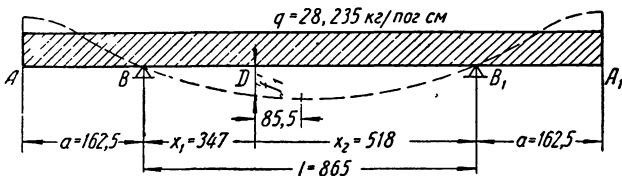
Схема нагрузки хребтовой балки гондолы с учетом реакции поперечных опор.
